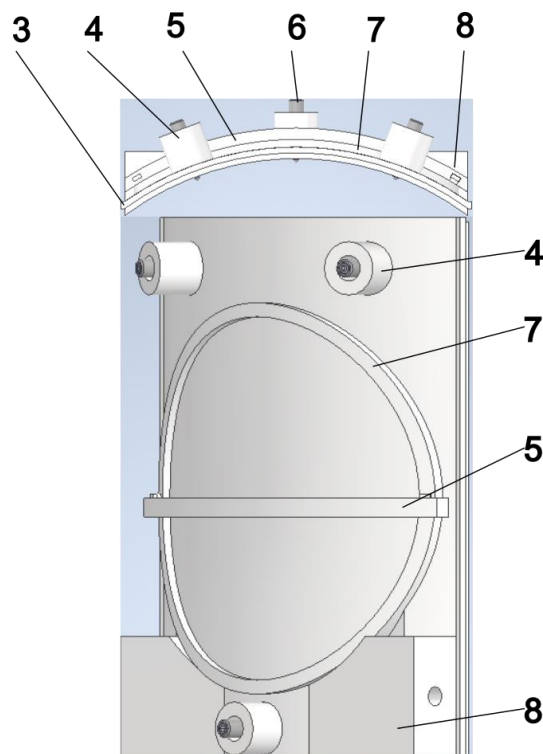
Obere Schnittstelle. 3) Grundplatte, 4) Aufnahme für Gewindeeinsatz 5) Balken, 6) Federbolzen, 7) Anschlagring Ladespule, 8) Aufnahme Gewindeeinsatz Gehäusebefestigung
